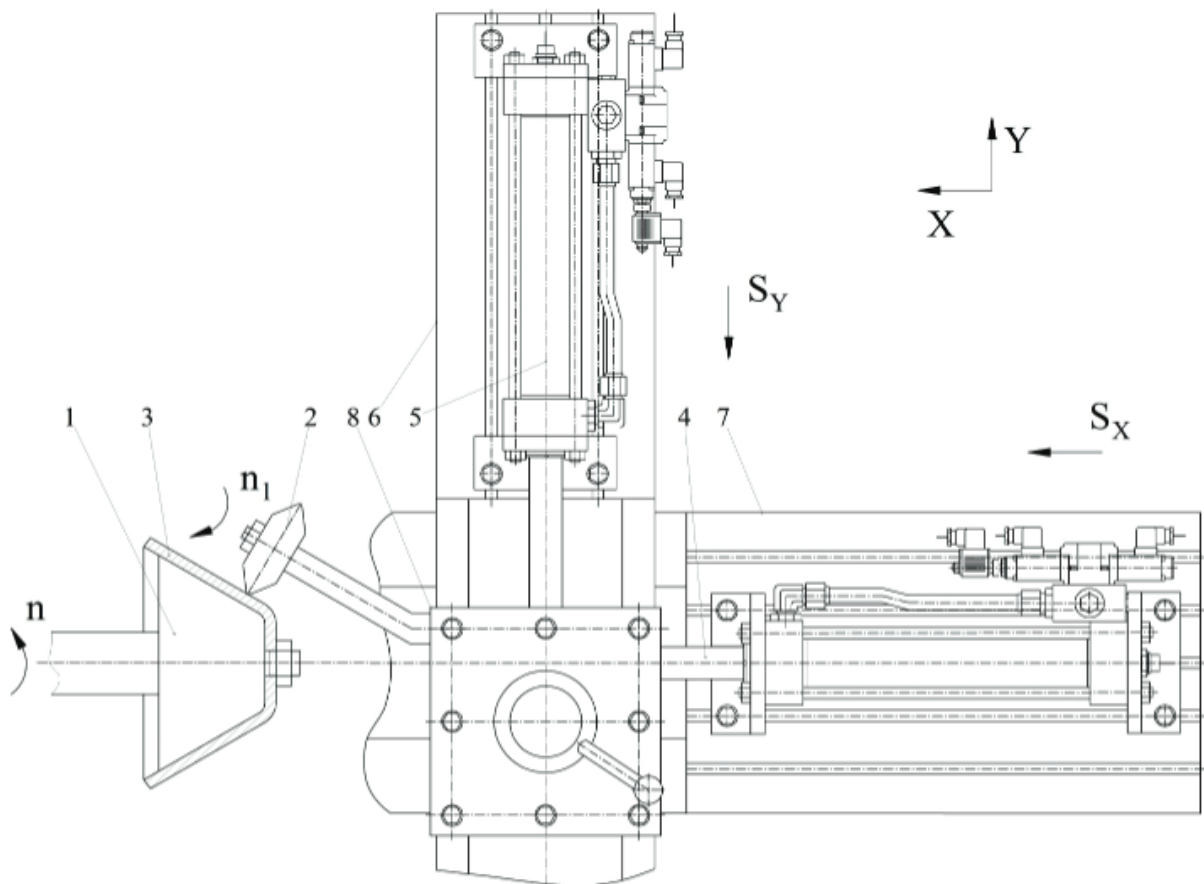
Схема виготовлення деталі ротаційною витяжкою за допомогою пристрою з мехатронним приводом
